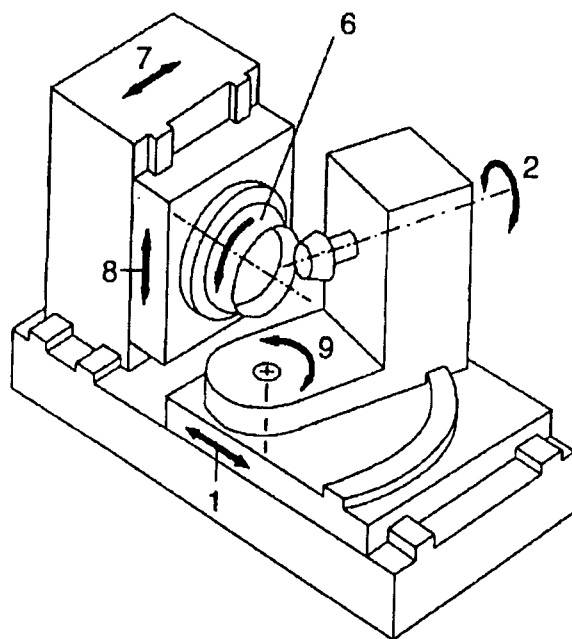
Frézovanie zubov kuželových kolies tvarovou kotúčovou frérou na univerzálnom frézovacom stroji
